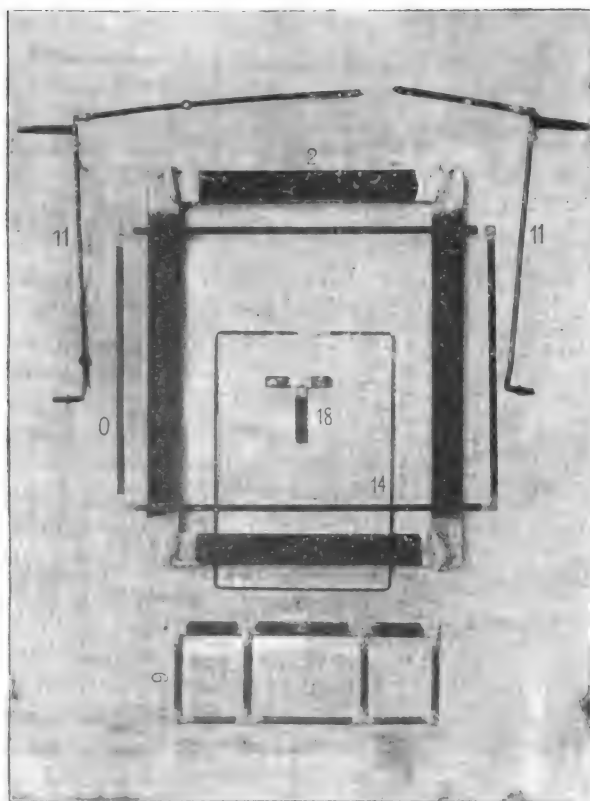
Échantillons des produits de soudure électrique.
